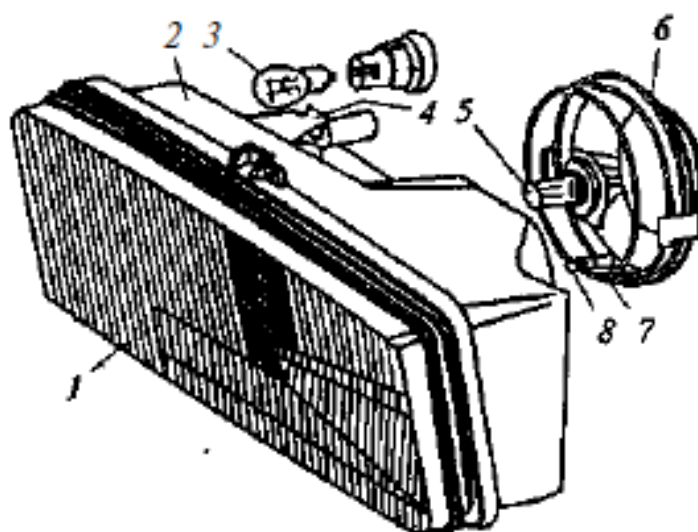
Блок-фара автомобиля ВАЗ-2105: 1 – рассеиватель; 2 – корпус; 3 – лампа указателя поворота; 4 – скоба для крепления; 5 – галогенная лампа основного света; 6 – кожух; 7 – уплотнитель; 8 – лампа габаритного света
